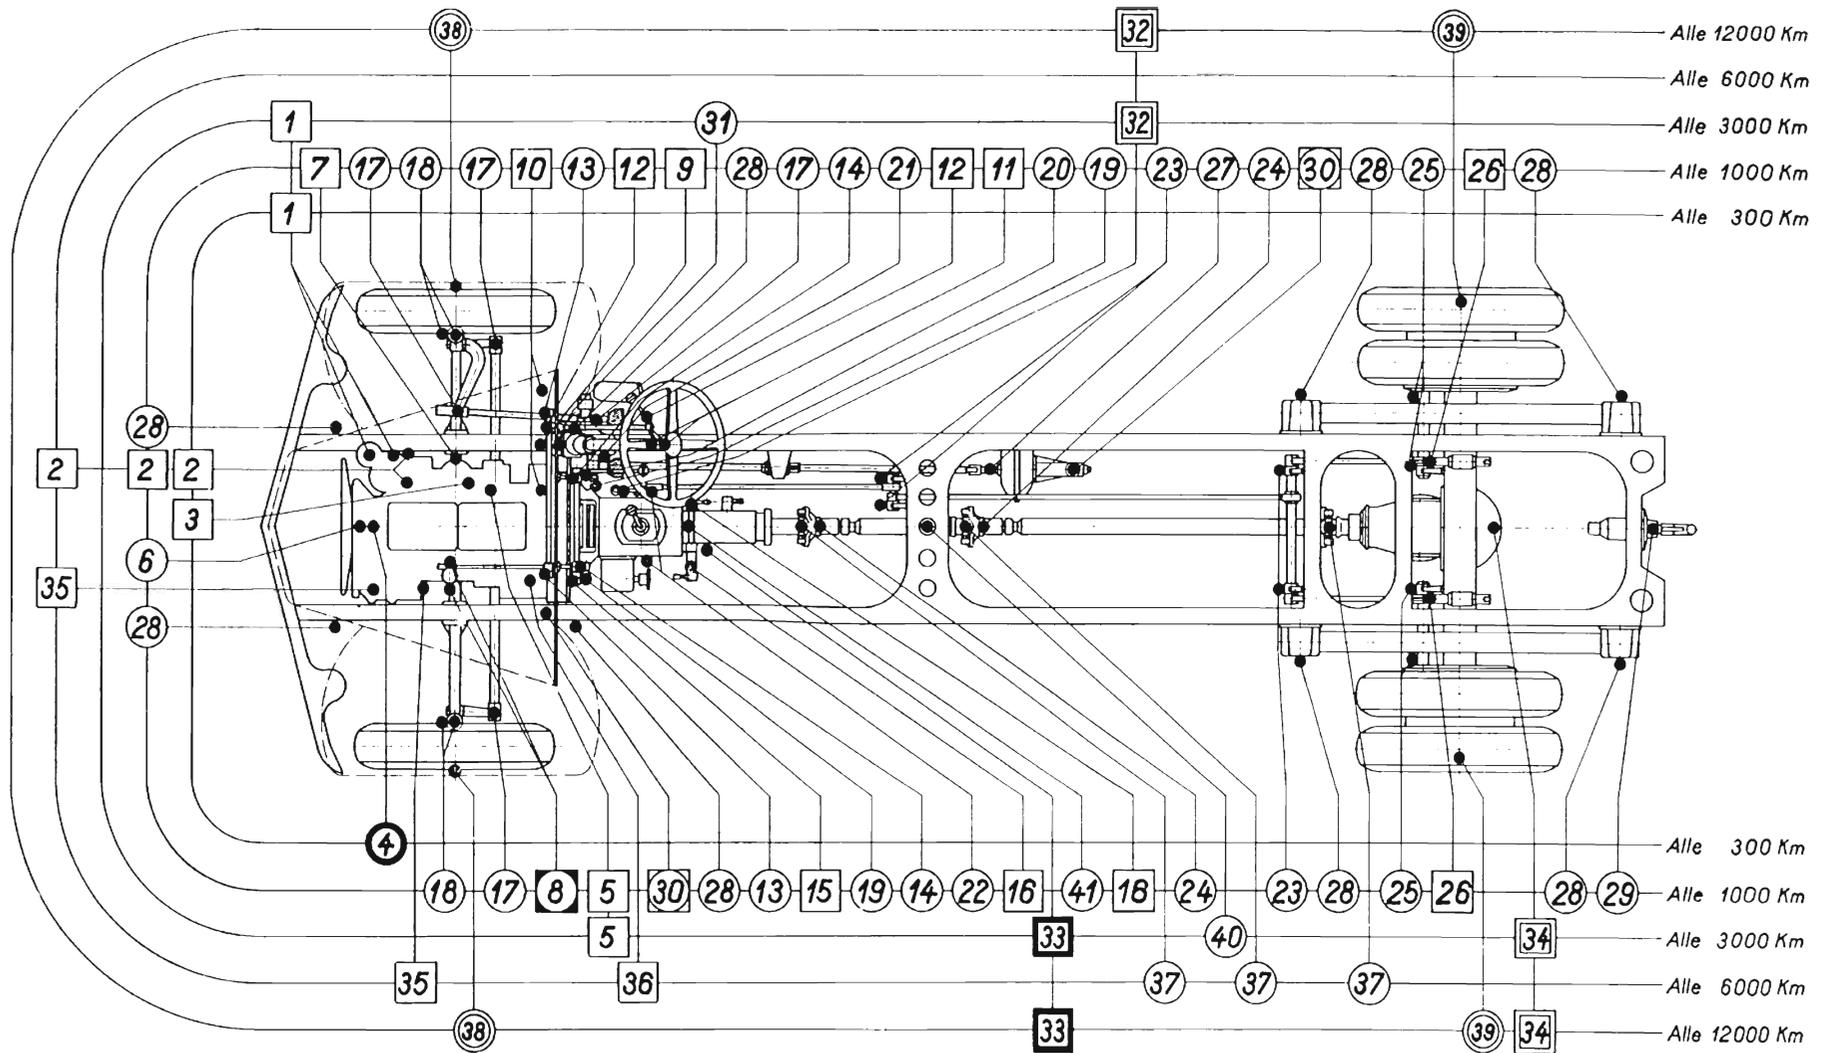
Schmierplan zu RD-Motor und Chassis Type AM 44
